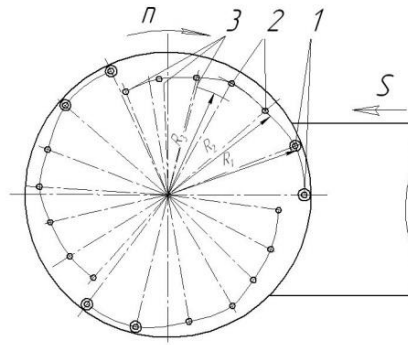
Схема розташування різальних елементів в корпусі фрези
